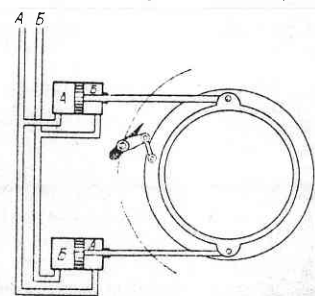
Схема привода направляющего аппарата с двумя цилиндрическими сервомоторами
